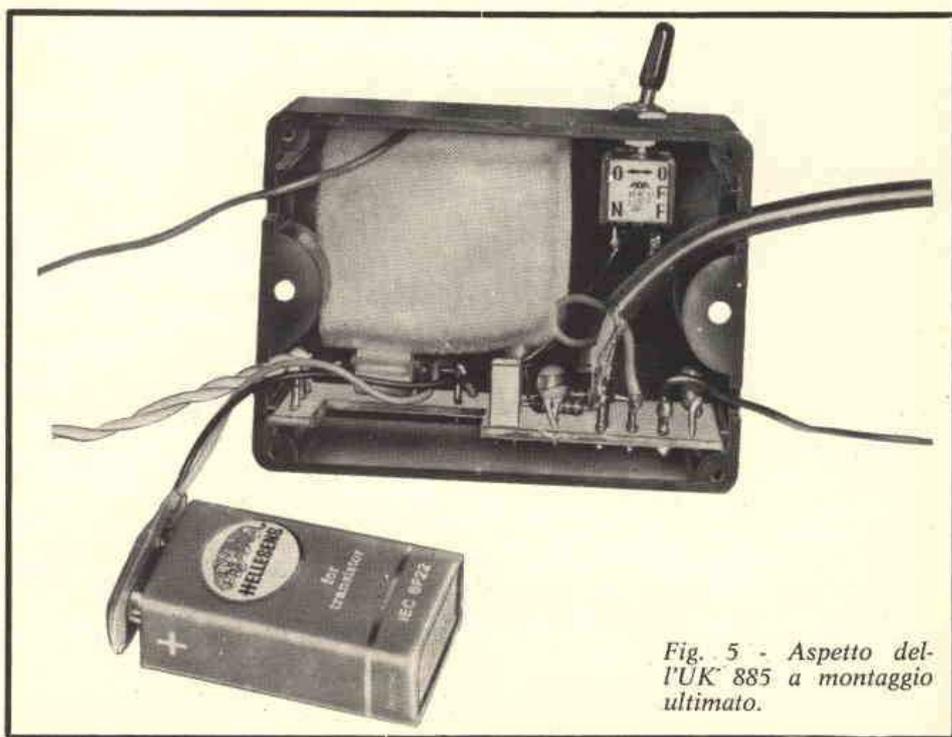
Aspetto dell'UK 885 a montaggio ultimato.
